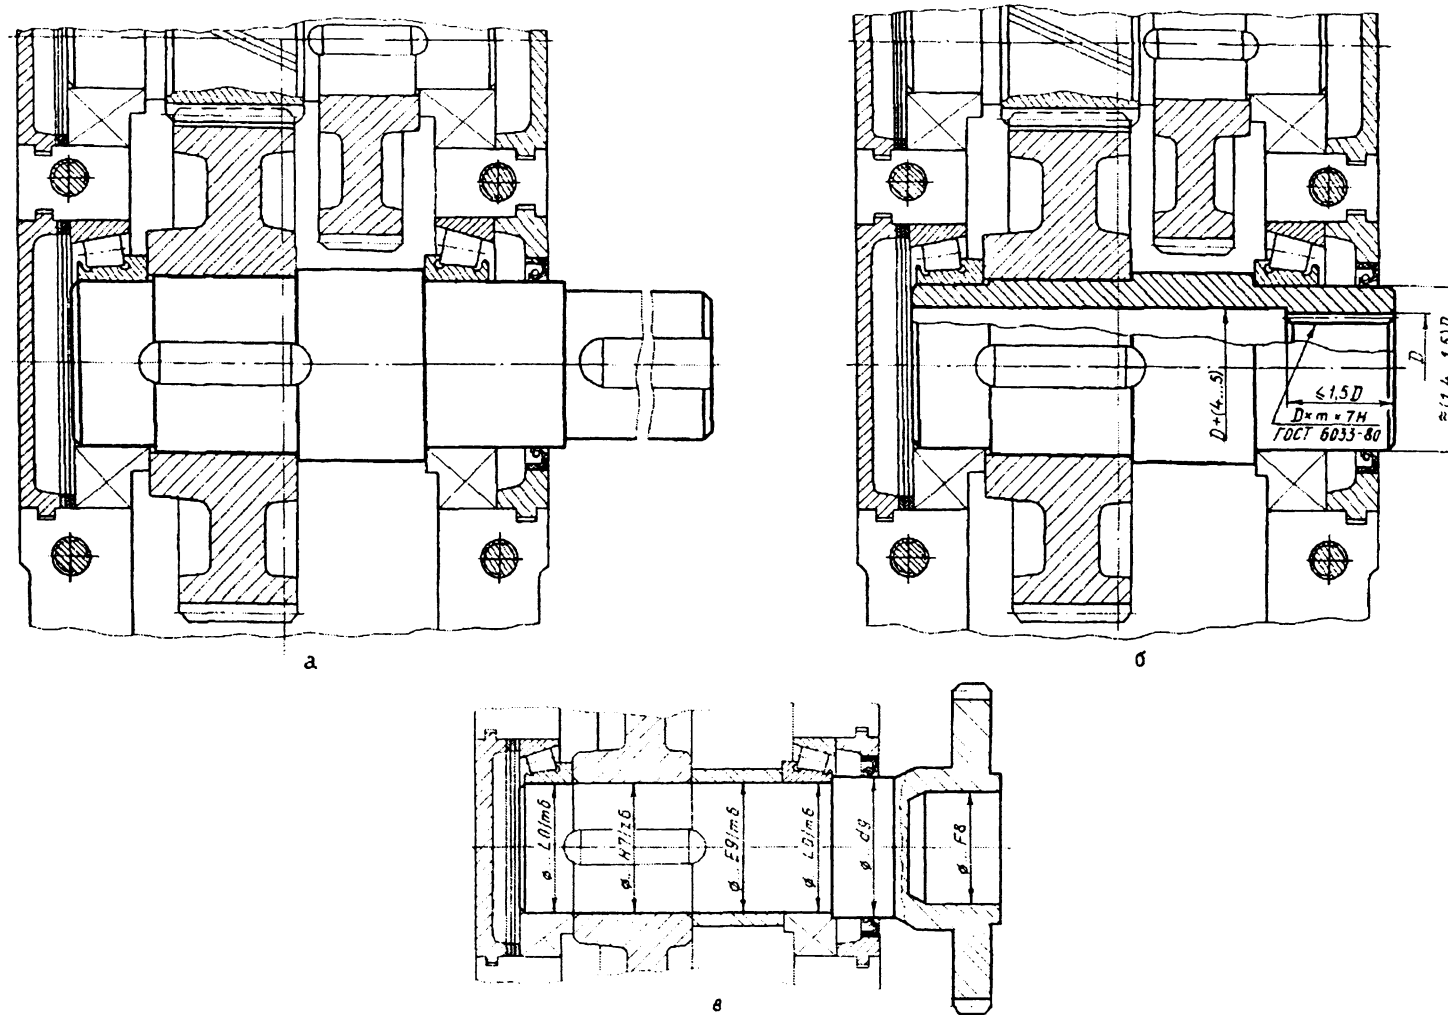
Тихоходные валы цилиндрических двухступенчатых зубчатых редукторов, выполненных по развернутой схеме:
